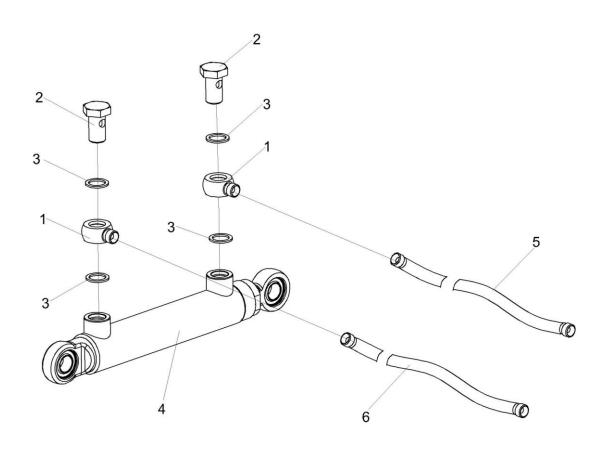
Гидроцилиндр КЗК 0602060-02
